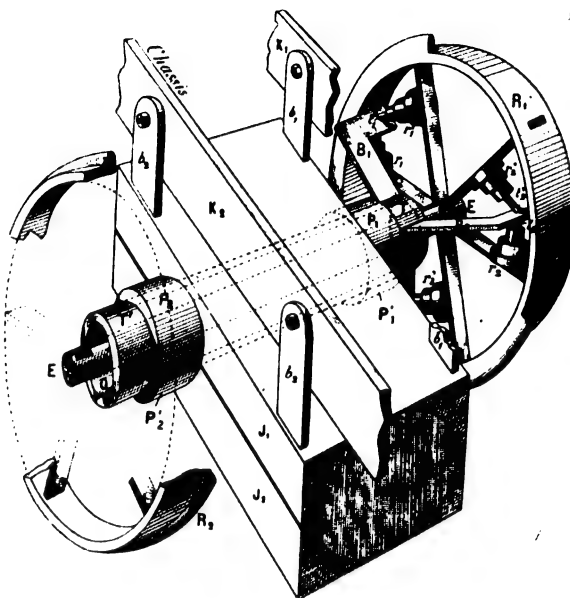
Vue perspective schématique d'un essieu moteur.
